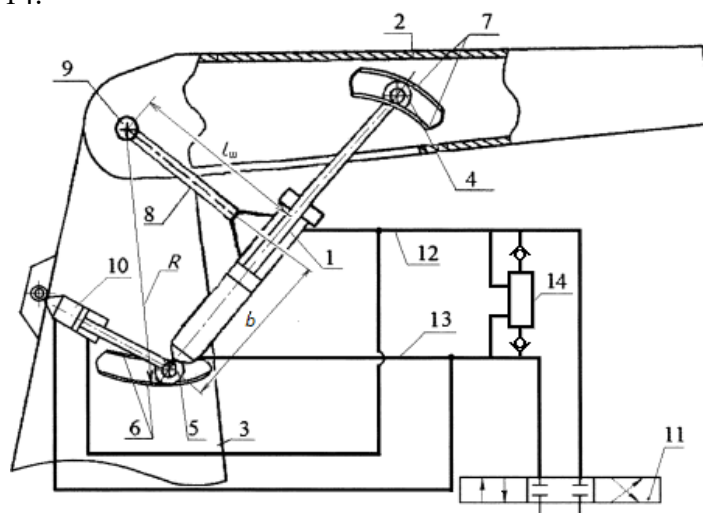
Гидрокинематическая схема механизма подъёма стрелы манипулятора: 1 — гидроцилиндр; 2 — стрела; 3 — колонна; 4 и 5 — ролики; 6 и 7 — направляющие; 8 — штанга; 9 — ось; 10 — дополнительный гидроцилиндр; 11 — распределитель; 12 и 13 — гидролинии; 14 — демпфер
